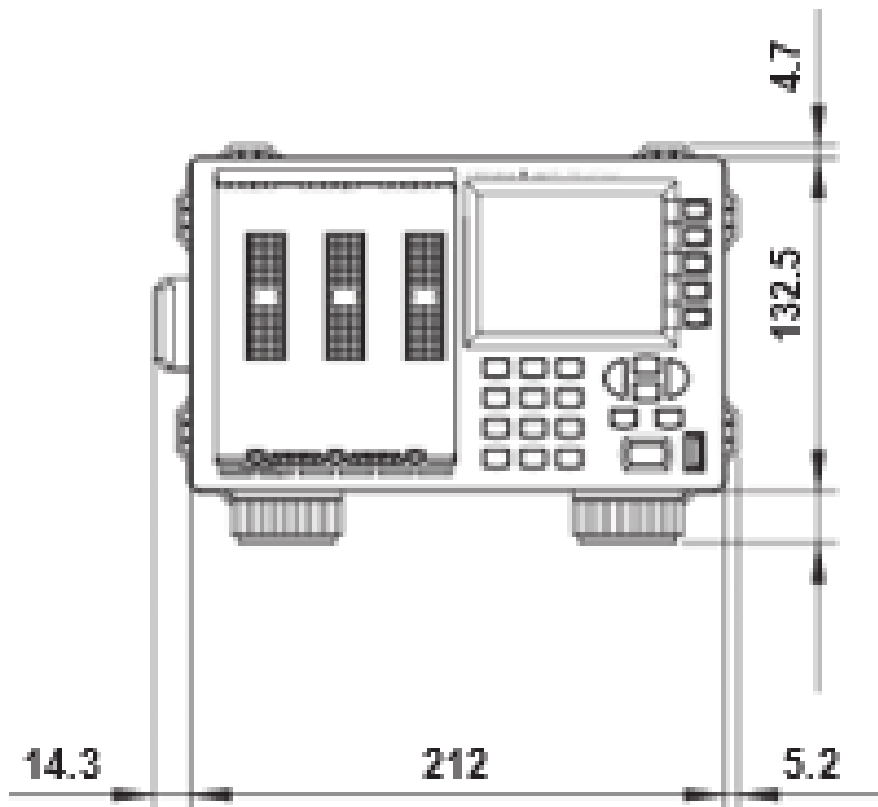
Dimensiones de la parte frontal del controlador de cuadros YOKOGAWA serie AQ2211. Fuente: [17].
